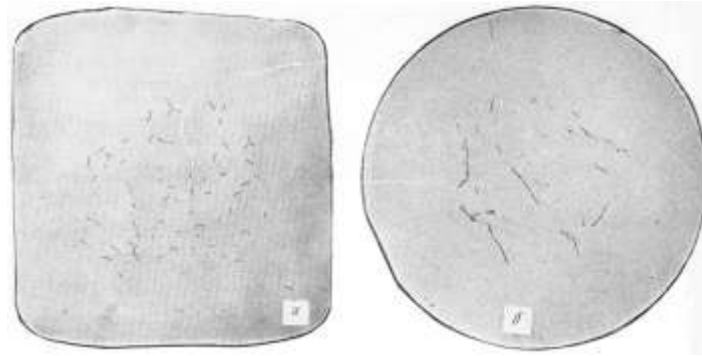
Флокены в макрошливах стали ШХ15 (типичный вид флокенов в стали перлитного класса):
